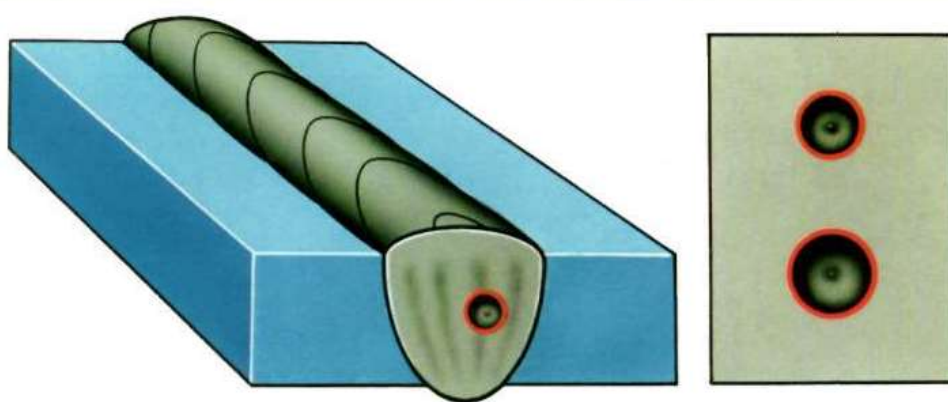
Дефекты сварного шва по типу газовой поры
